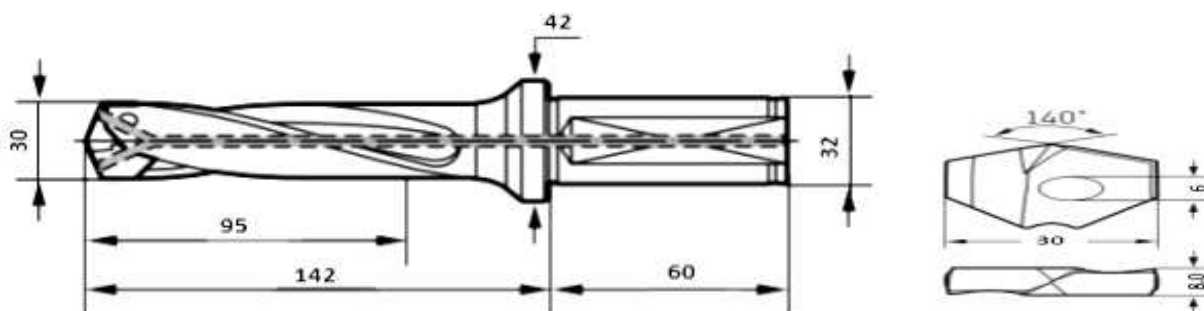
сверло В4013.F32.30.0.Z02.90R, пластина Р6001-D30.00R
